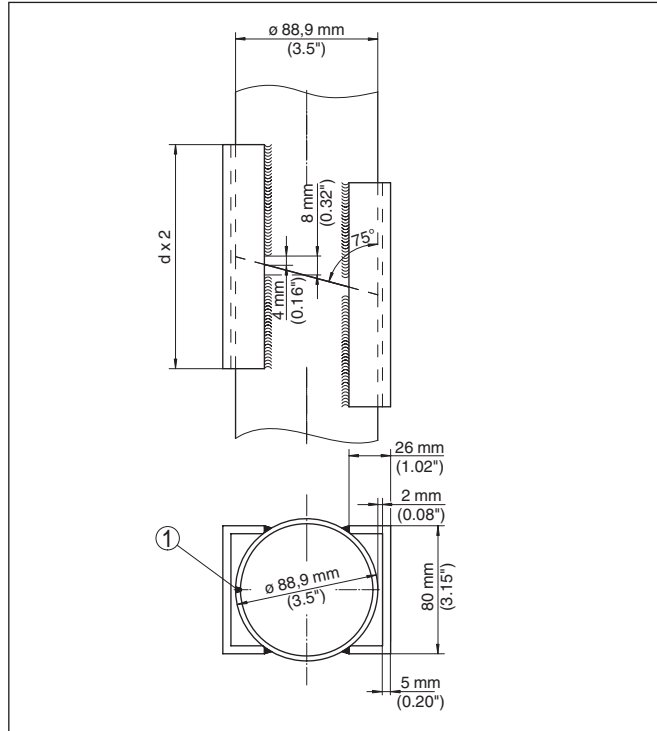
União soldada no prolongamento do tubo tranquilizador para diferentes exemplos de diâmetro
